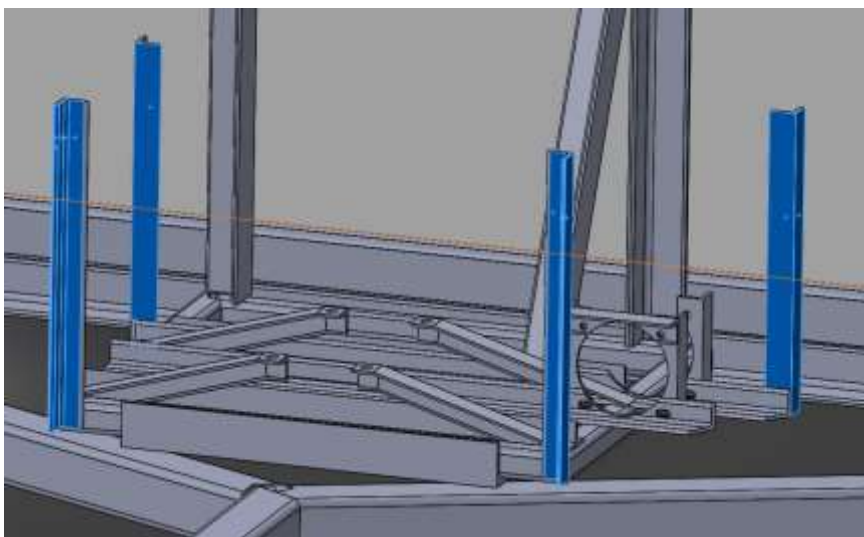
Cantoneiras verticais para fixação das redes de proteção
